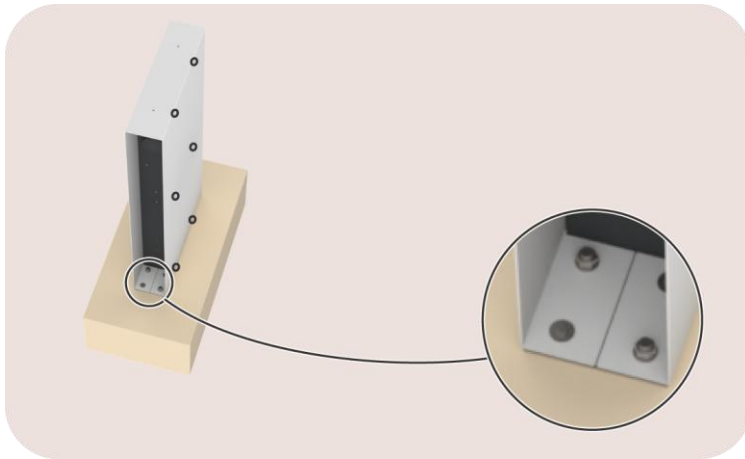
Vue sur les boulons qui maintiennent la plaque arrière et la plaque de sol.
